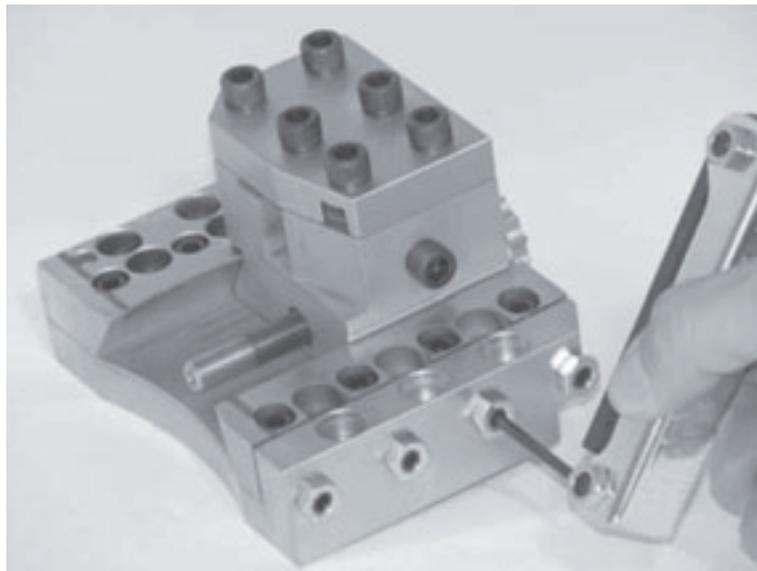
Reinstallare le viti di fissaggio e serrarle.
